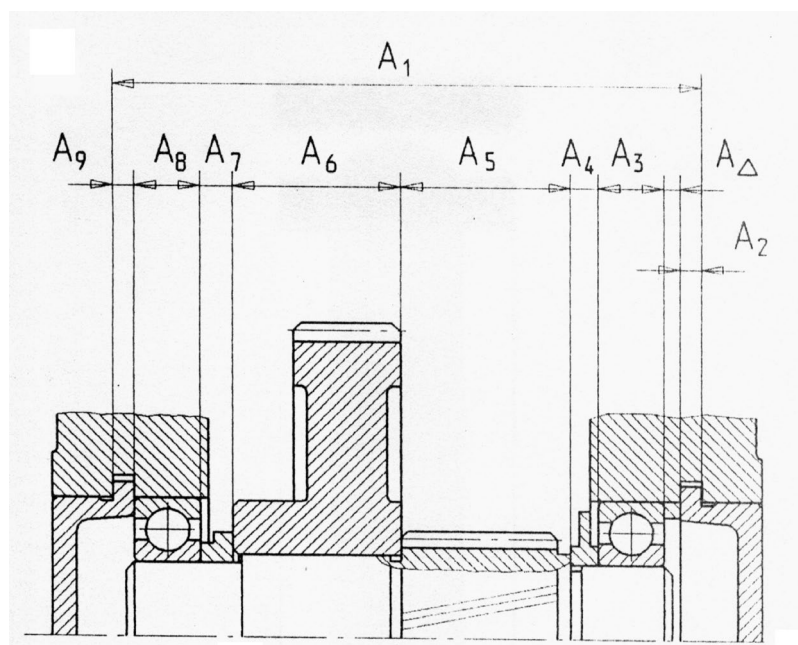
Сборочный чертеж узла и его размерная цепь
